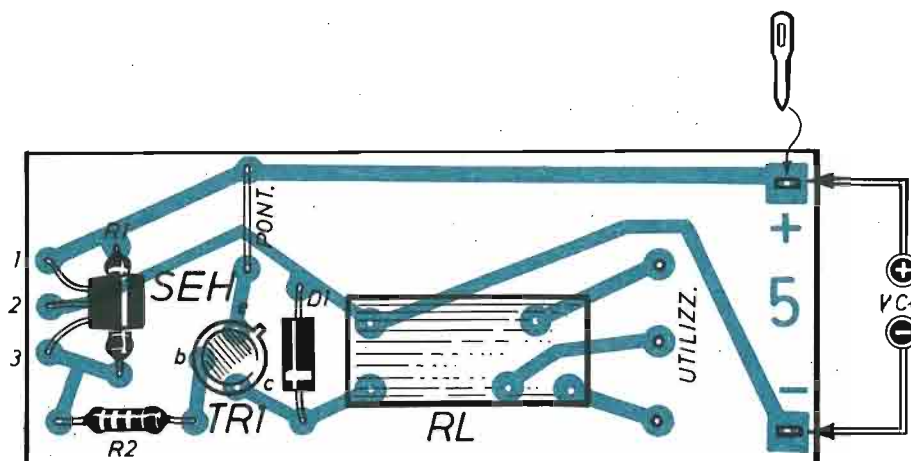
Montaggio del dispositivo di pilotaggio di un relé a 12 Vcc. La basetta supporto, di materiale isolante e di forma rettangolare, presenta le dimensioni di 3,5 cm x 9 cm.
